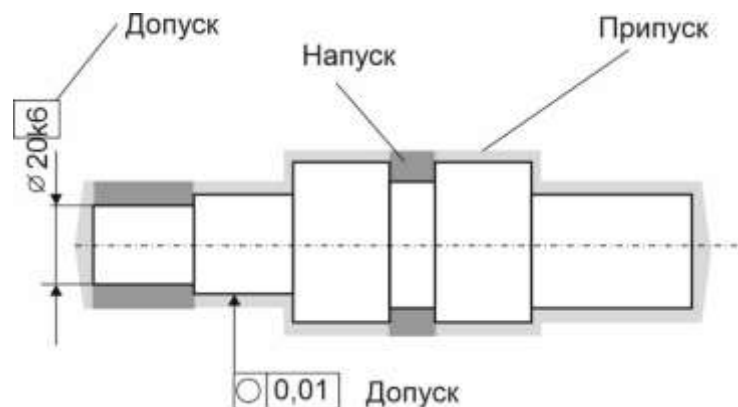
Припуски, допуски та напуски заготовки.
